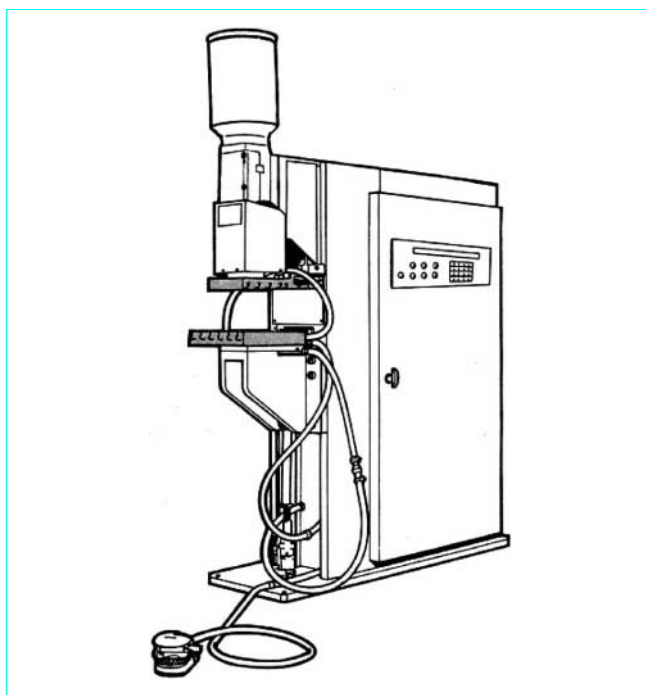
Soudage par bossages : presse à souder équipée de plateaux rainurés
